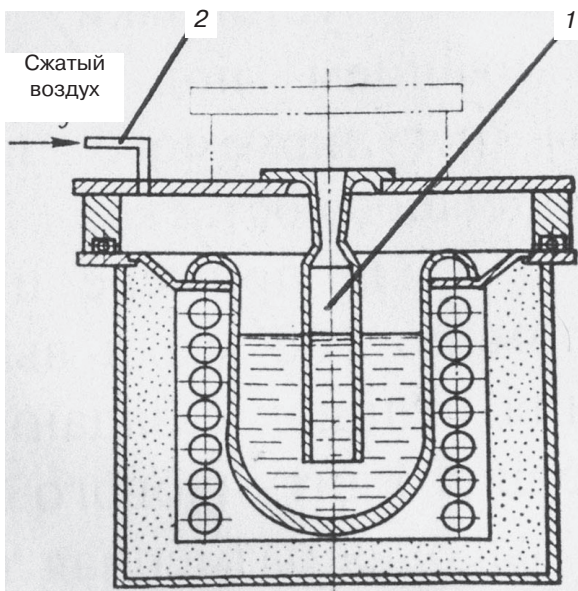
Схема заливочного агрегата установки литья под низким давлением: 1 – металлопровод; 2 – трубопровод
